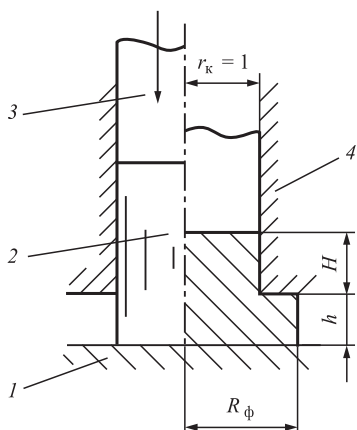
Схема радиального выдавливания заготовки: 1 — опора; 2 — заготовка; 3 — пуансон; 4 — контейнер
